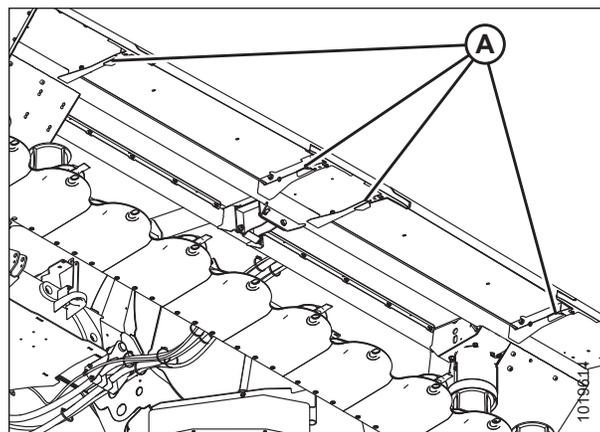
Дверки ножевого бруса R116 — Вид снизу вверх
